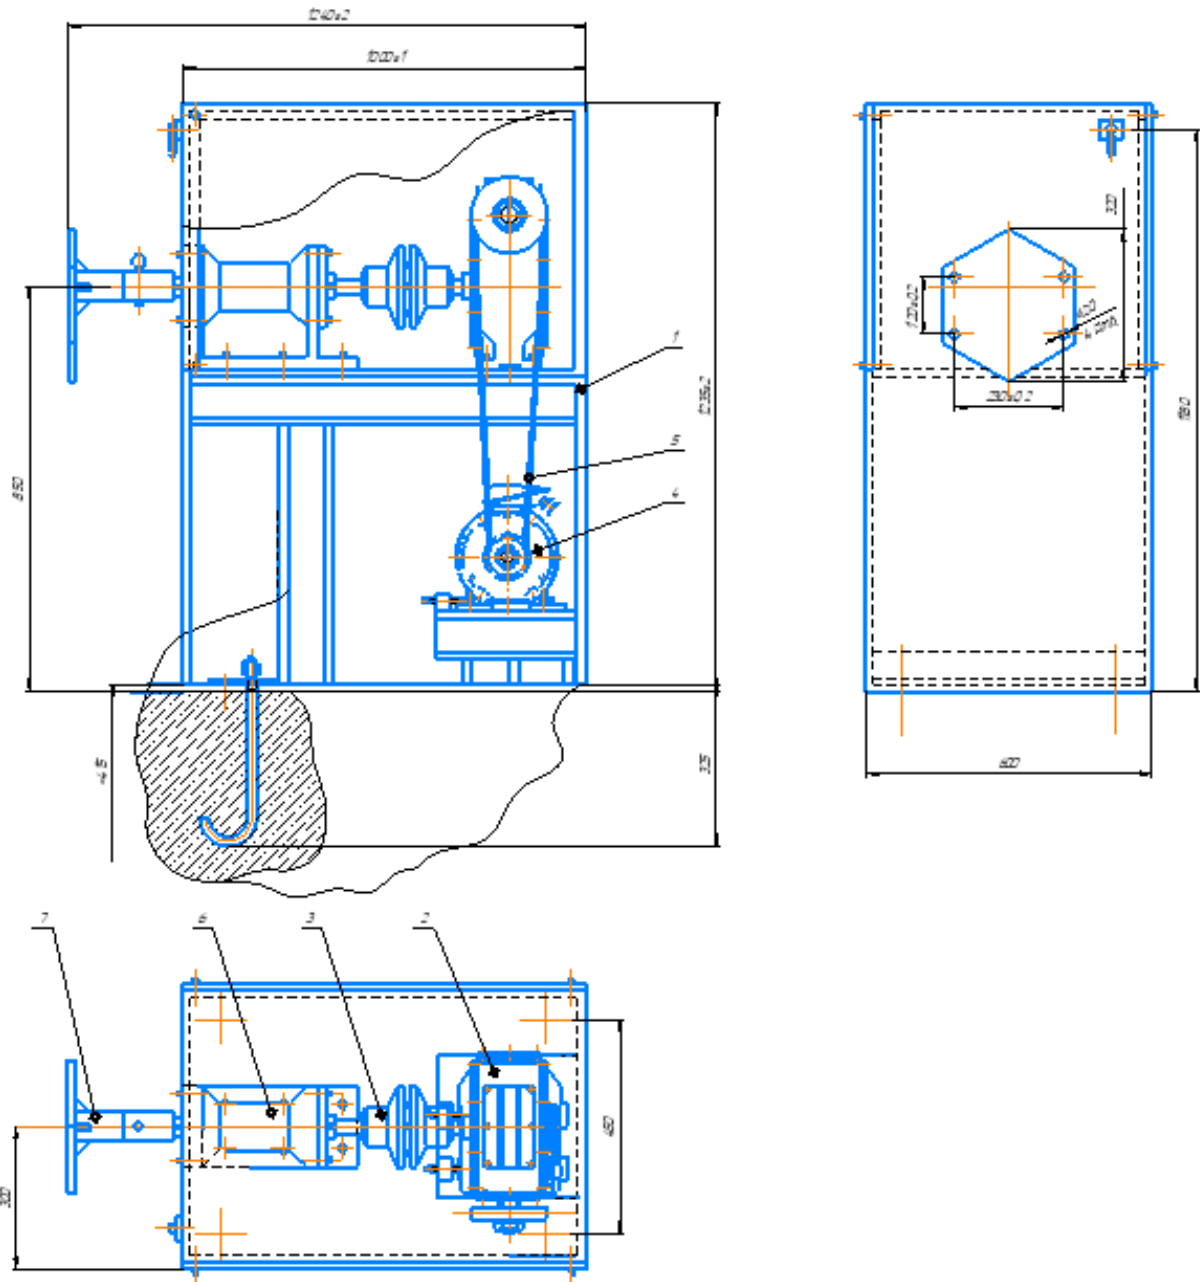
Універсальний стенд для монтажу та демонтажу двигунів:
